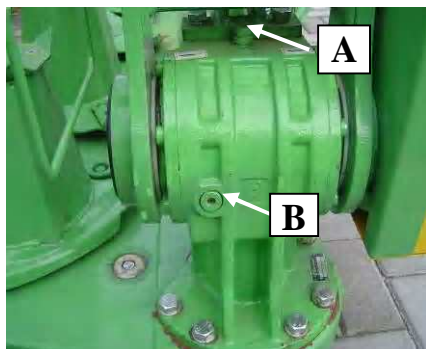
Заливная пробка A и сливная контрольная пробка B редуктора
